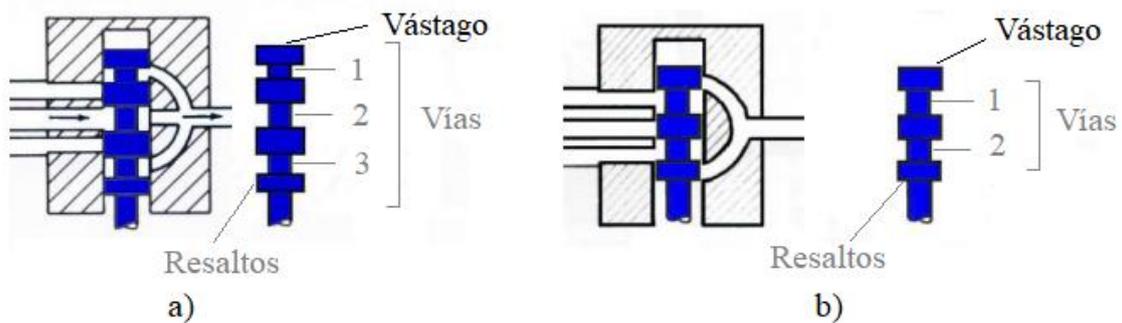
a) Configuración centro abierto, b) configuración centro cerrado
